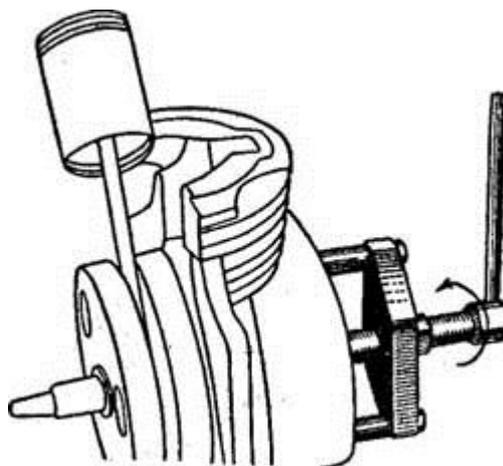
Выпрессовка коленчатого вала из левой половины картера силового агрегата
